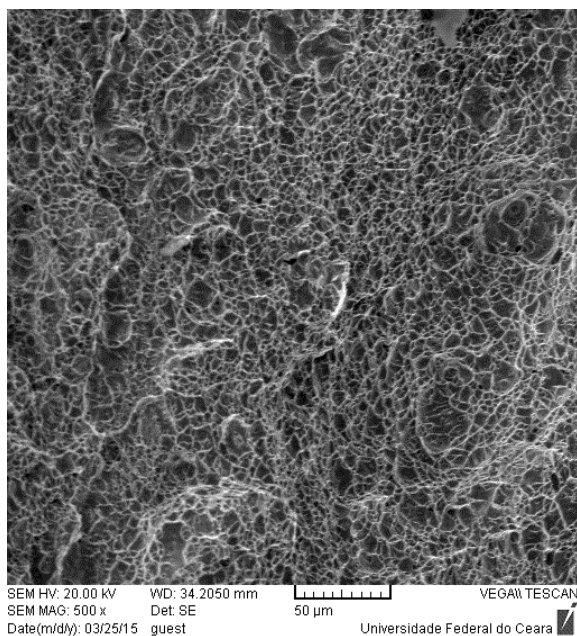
Microscopia eletrônica de varredura (MEV). Superfície de fratura após ensaio de impacto de Charpy. Amostra com entalhe no metal de solda *Maraging 350*. 500X.
